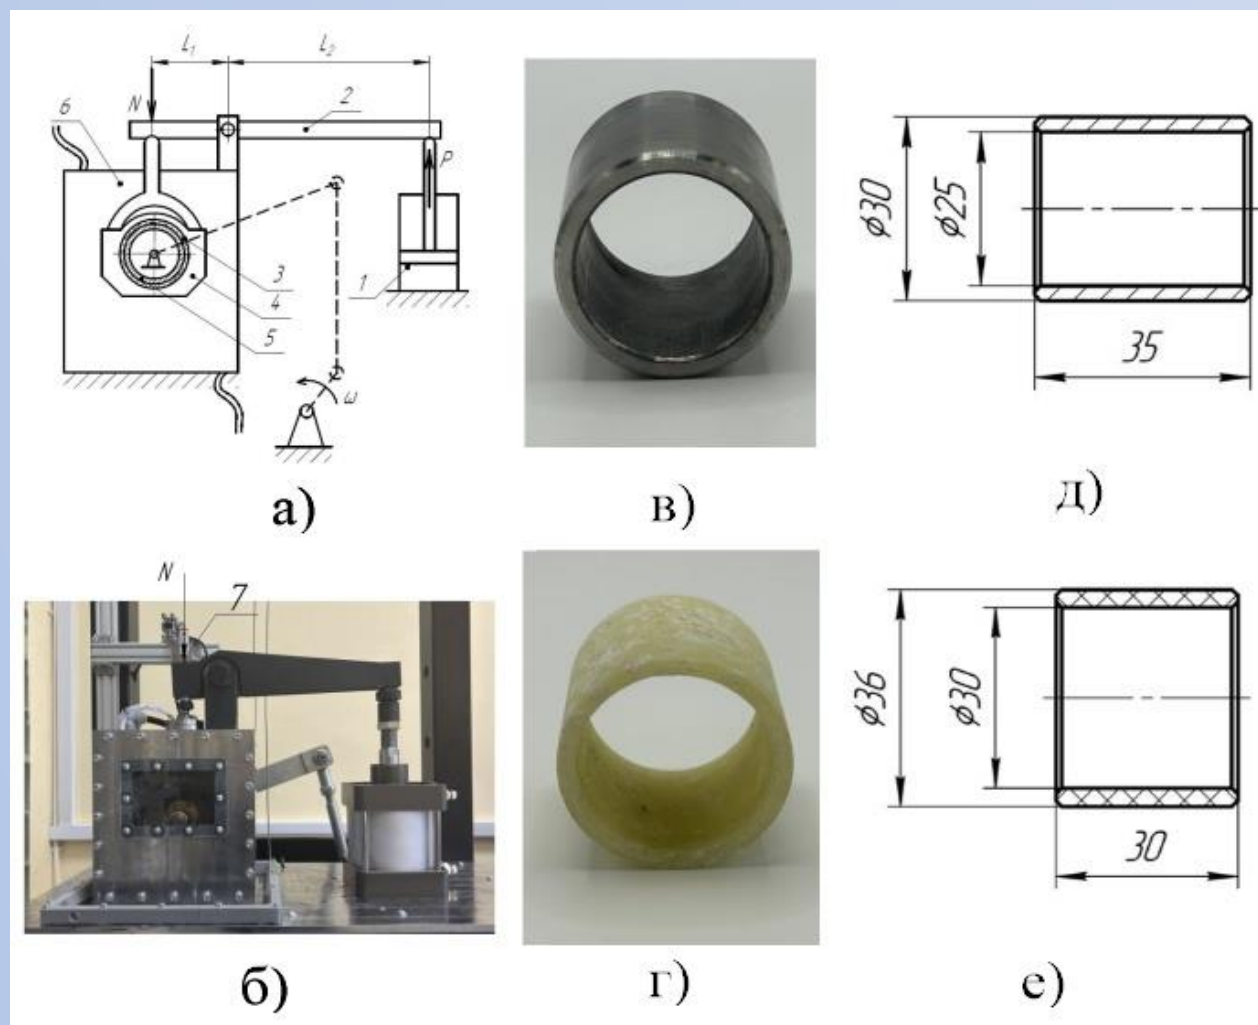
Кинематическая схема стенда (а) и внешний вид камеры для испытаний (б) машины трения «ИМАШ - ШАРНИР». Чертежи и фото контробразца (в и д соответственно) и образца (г и е соответственно)
